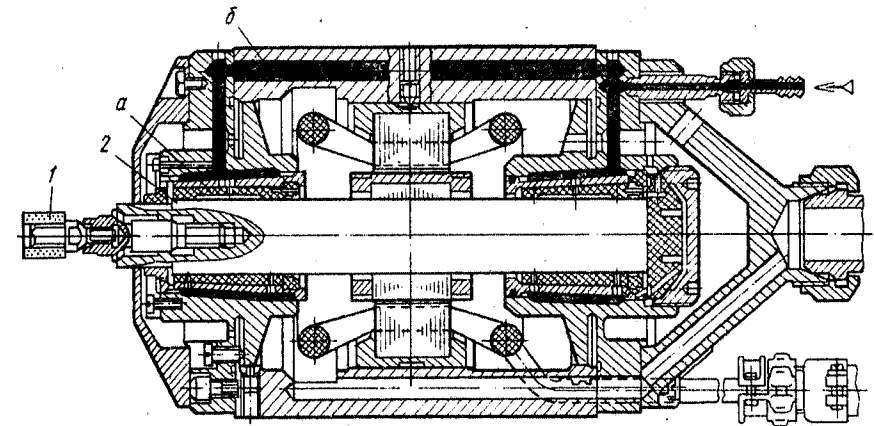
Шлифовальный шпиндель на аэроэстатических подшипниках
